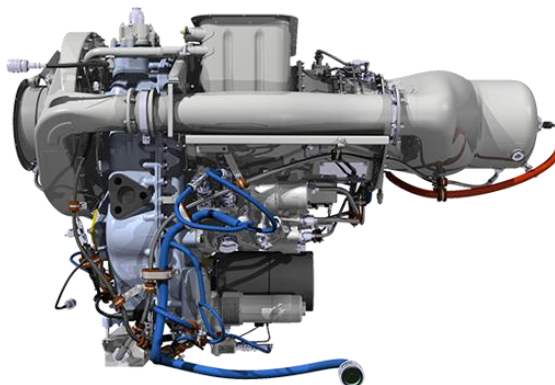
Koncept motoru řady H80 s planetovou převodovkou pro zástavby do rotorových letadel
